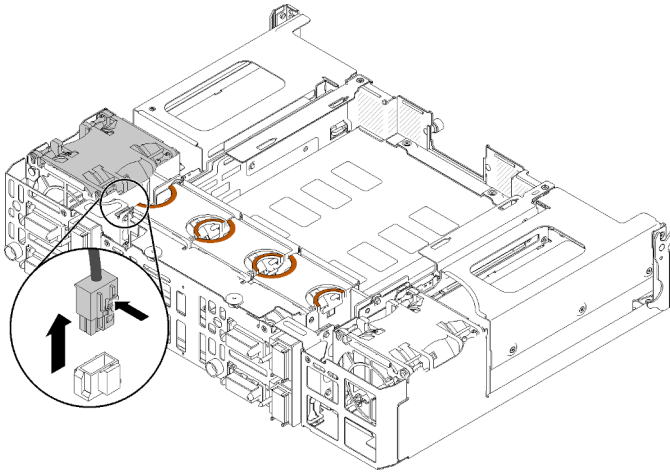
Desconexión del cable del ventilador del PIOR izquierdo
